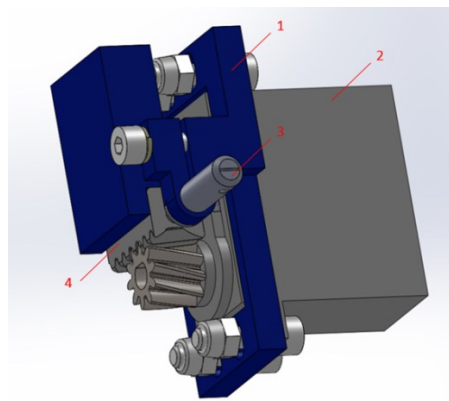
Обрезной механизм: 1 – кронштейн; 2 – серводвигатель; 3 – направляющая; 4 – рейка
